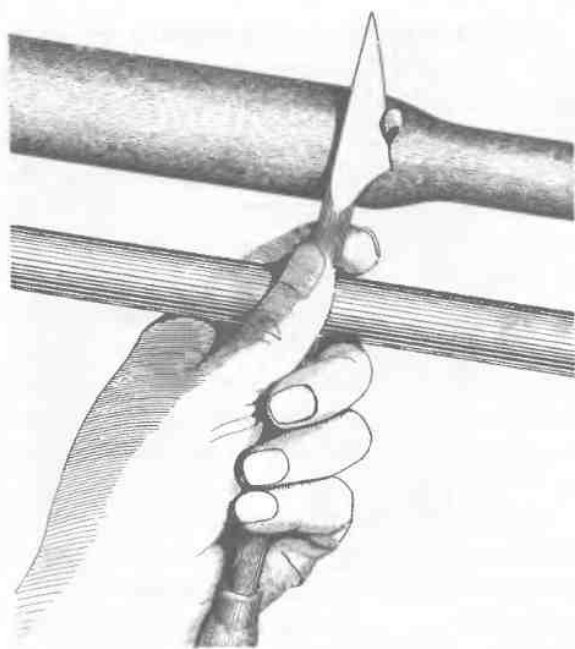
Один из приемов захвата левой рукой инструмента и подручника при работе на токарном станке (вид со стороны точильщика)
